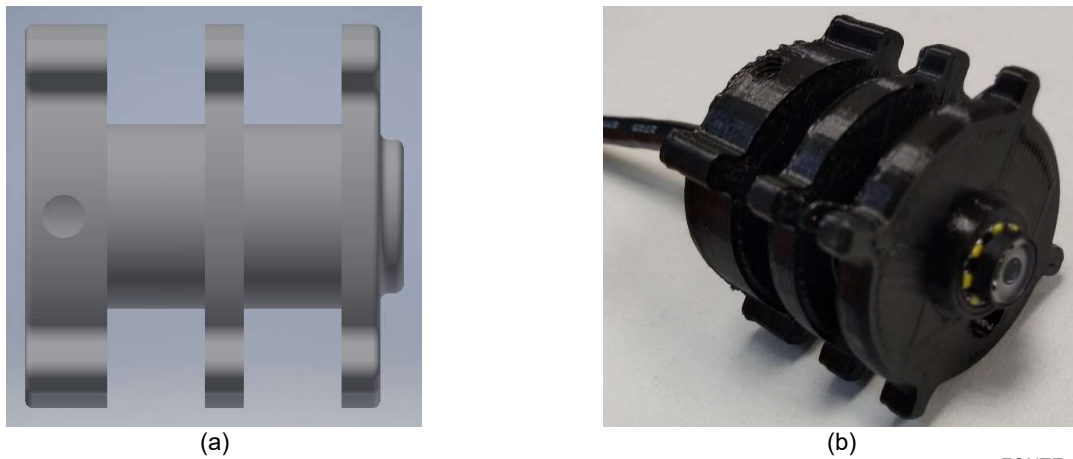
Módulo de inspeção: (a) projeto 3D e (b) conjunto montado
